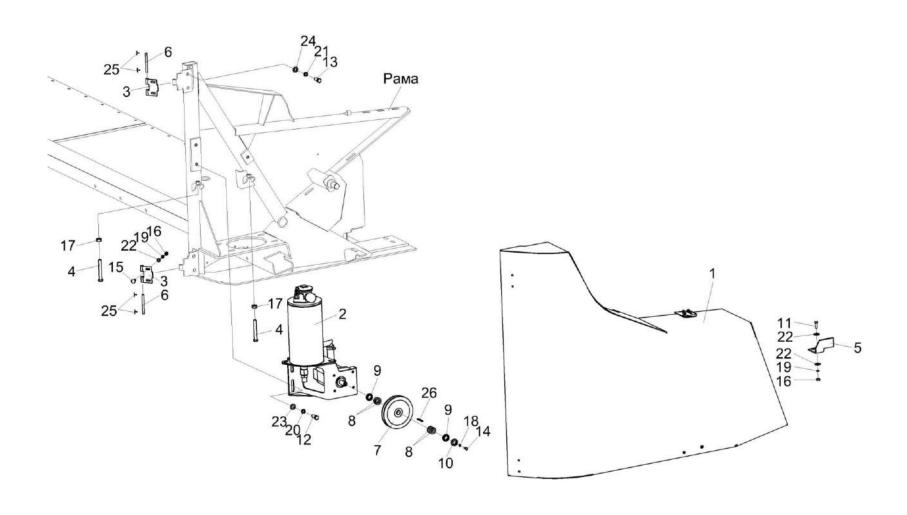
Приспособление для уборки рапса КЗК-9-1540000А (лист 3)
